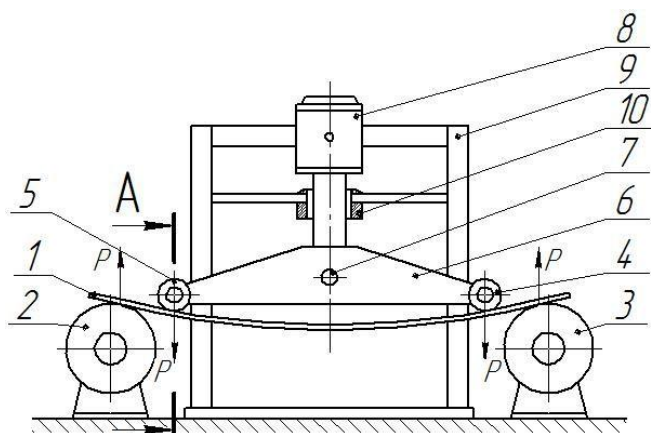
Конструкция машины для изгиба заготовок с двумя роликами, установленными на балке, опёртой на шарнир
